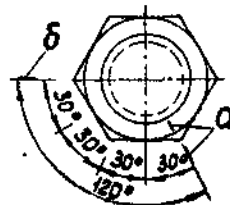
Нанесение меток при затягивании гайки крышки цилиндра
